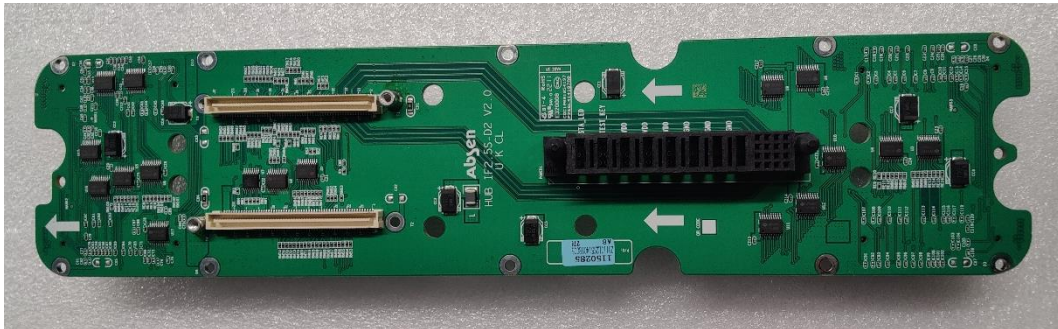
Hub Board Rückseite mit Steckplatz für Receiving Card und Stromversorgung¹¹³
